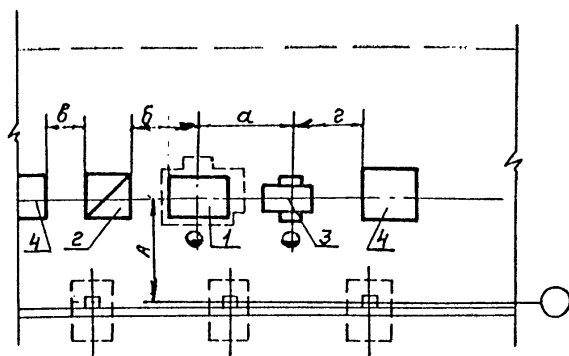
Схема расположения штамповочных линий на базе винтовых прессов с дугостаторным приводом:
